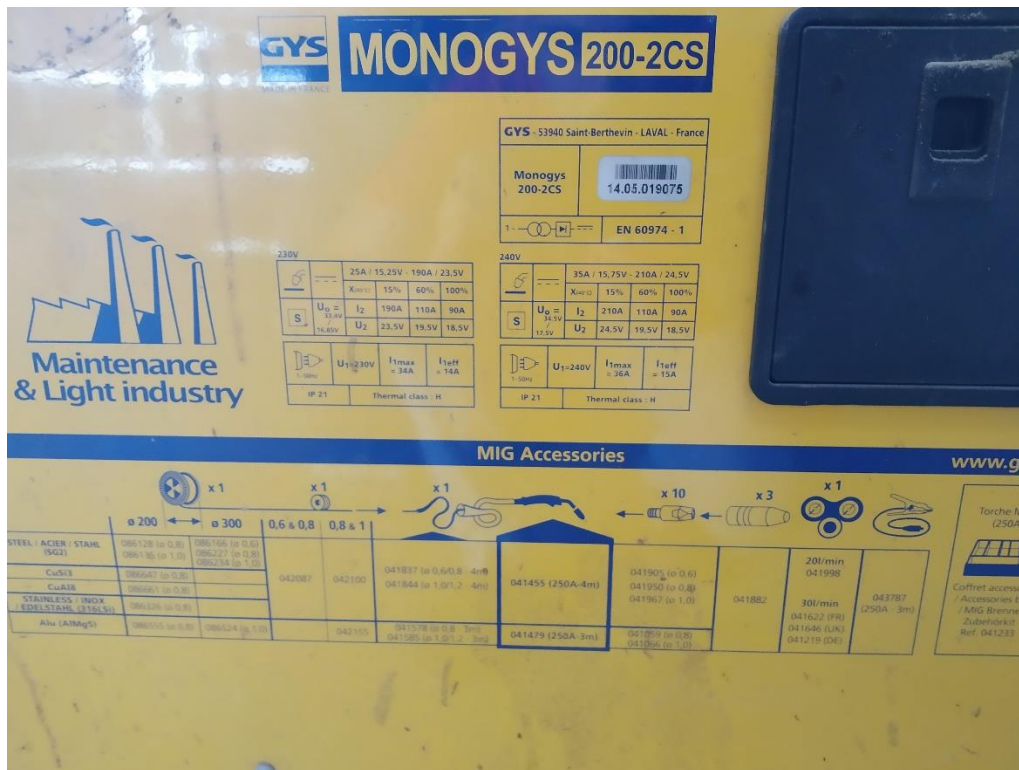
Equipo de soldadura MIG utilizado para el proceso de soldeo de la estructura.
